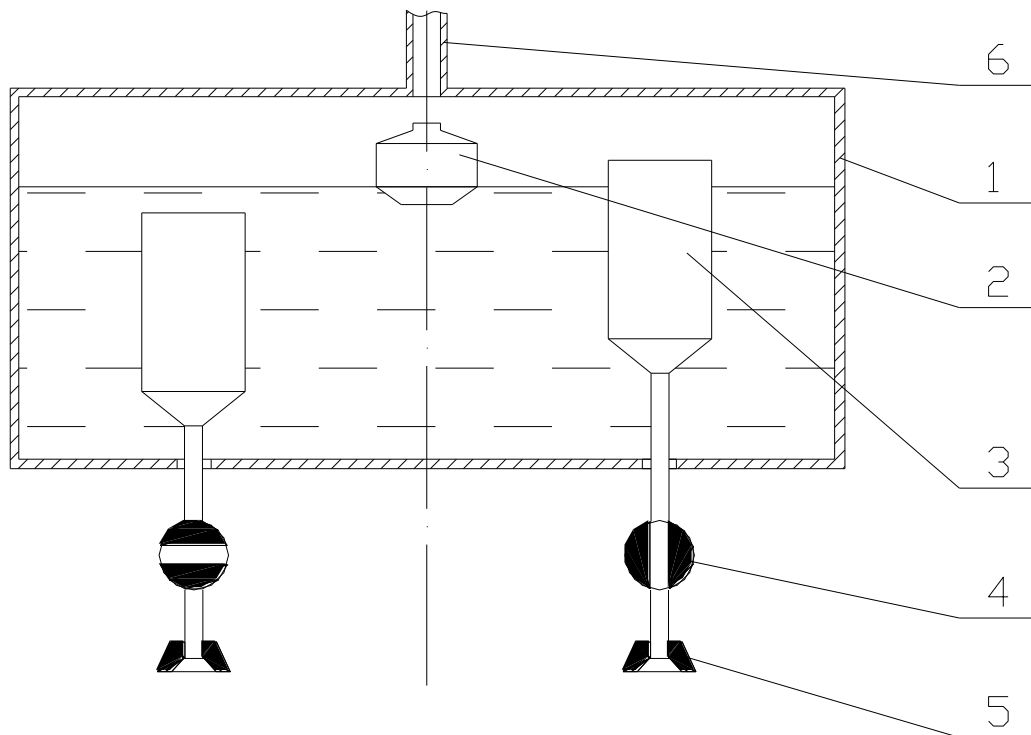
Схема роботи розливочного пристрою, який працює за принципом дозування по об'єму.
